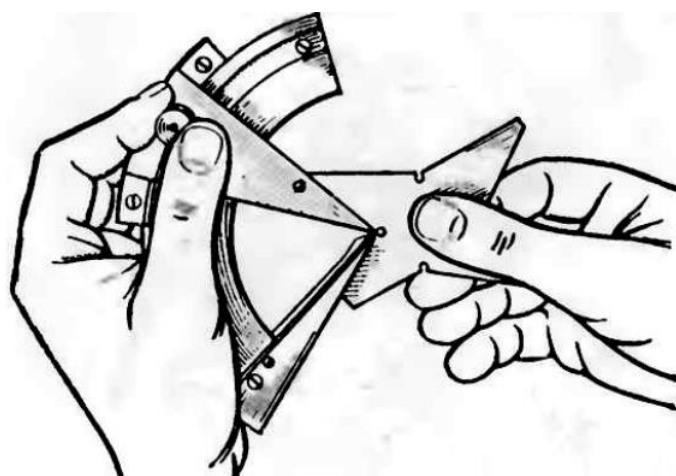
Установка угломера относительно внутреннего угла незакрепленной детали при помощи микроподачи
